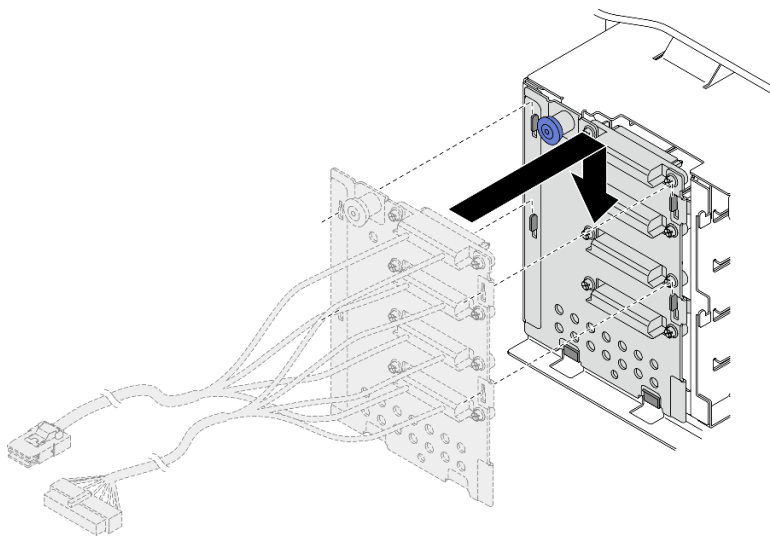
Installation de la plaque arrière d'unité remplaçable à chaud 3,5 pouces
